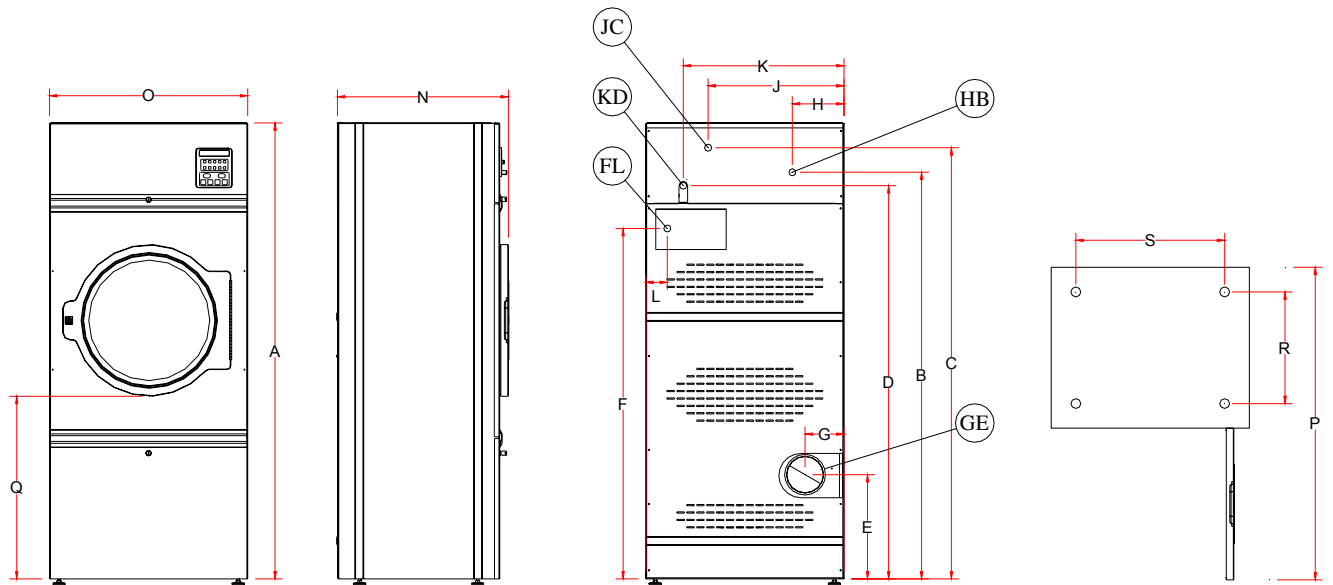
Dimensioni e collegamenti / Dimensions and connections / Dimensions et branchements /
